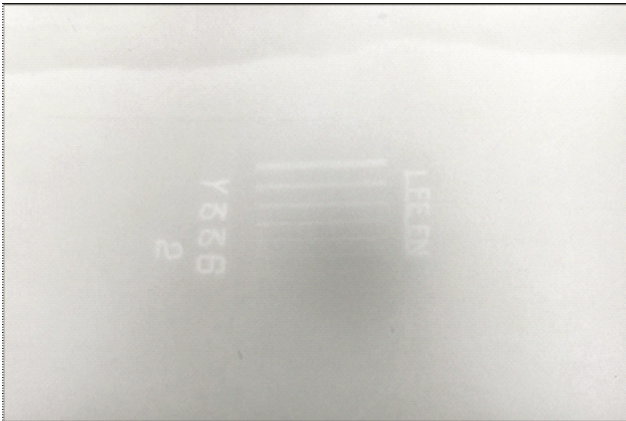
Obraz radiogramu obudowy wirnika odlew żeliwny.
